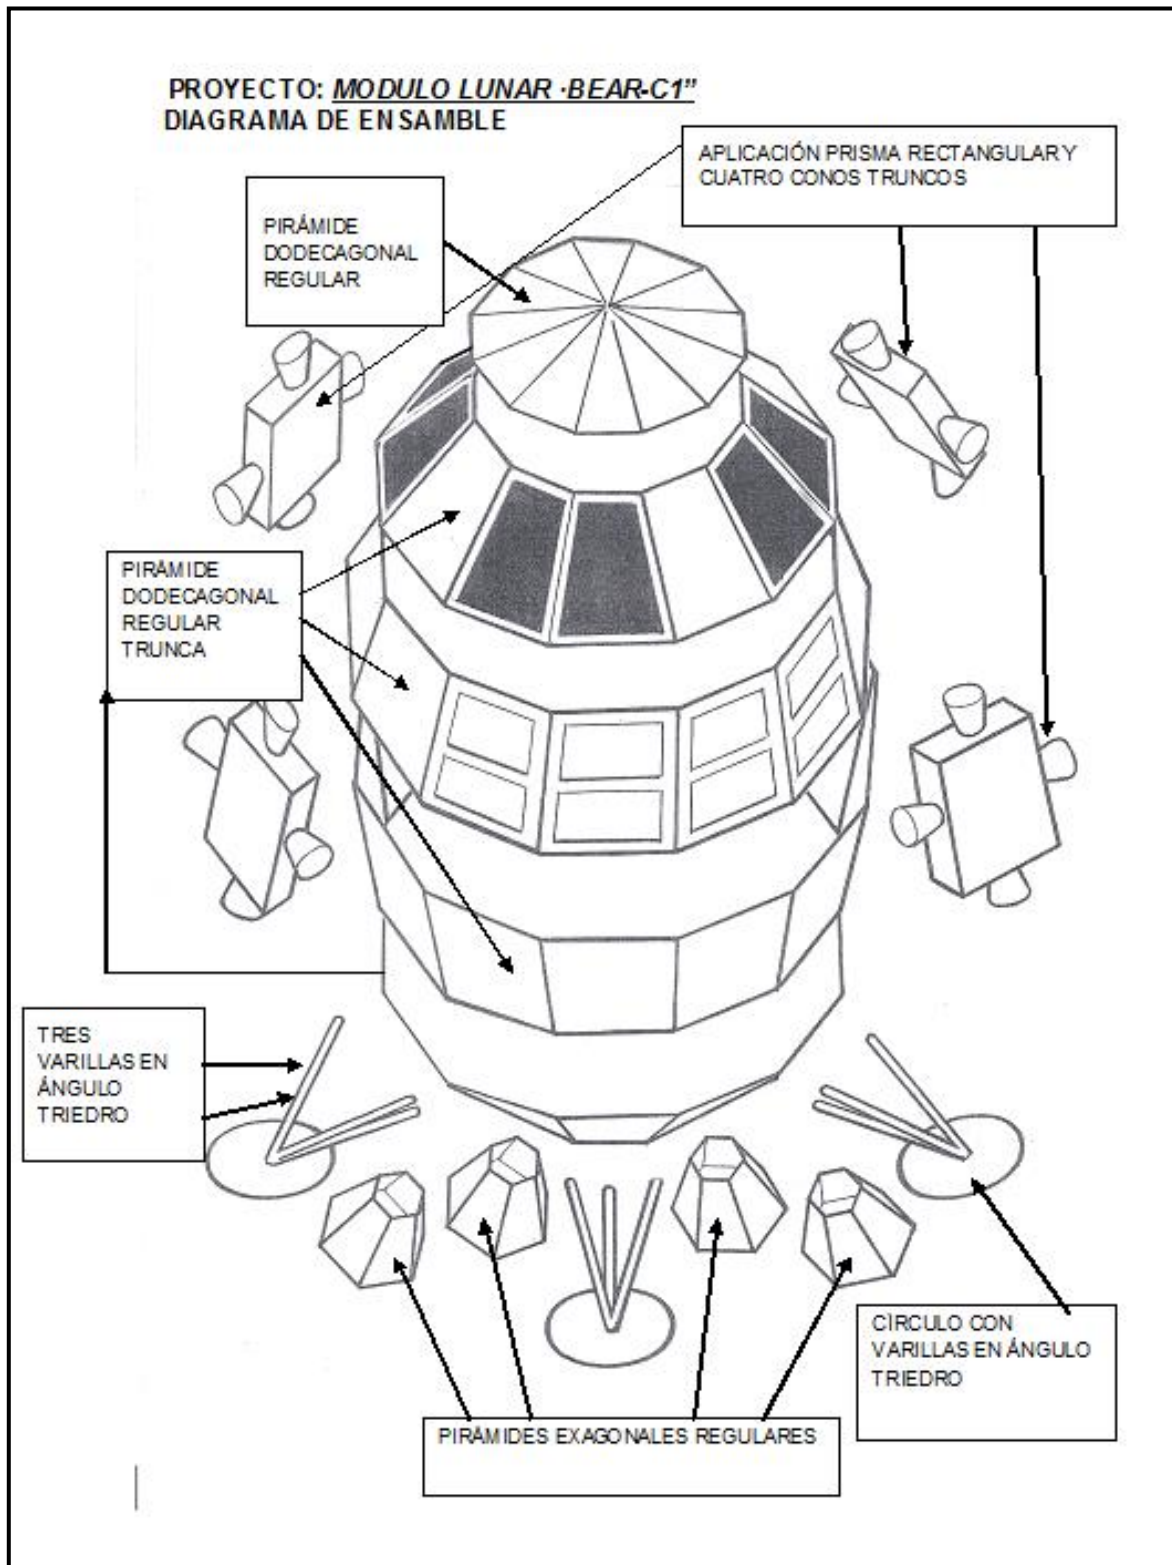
Práctica 30, Modulo Bear, vista explosionada
